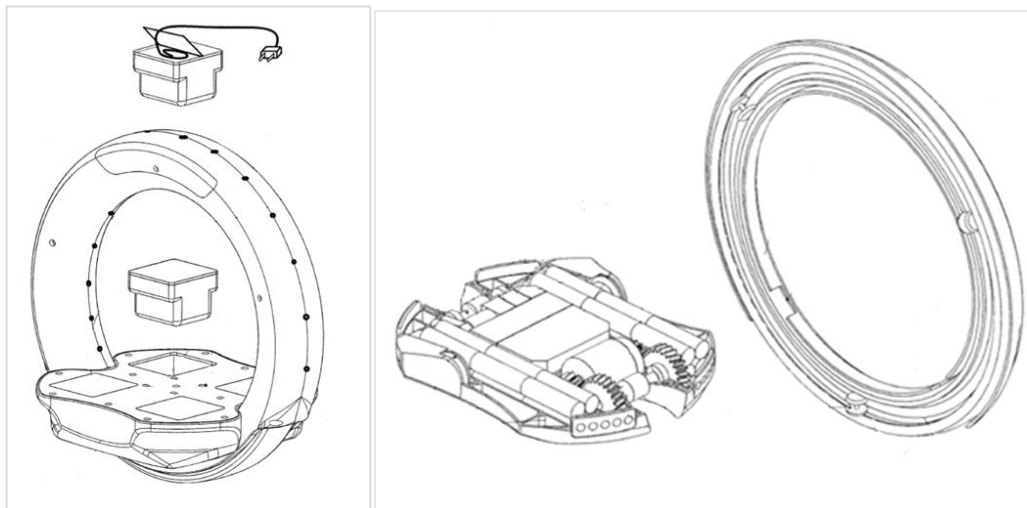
Общий собранный вид и внутренний «разобранный» вид моноколеса [21]
